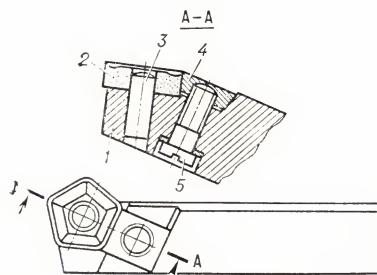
Резец с многогранной непереключаемой твердосплавной пластинкой: 1 — державка; 2 — пластинка; 3 — штифт; 4 — клин; 5 — винт.
